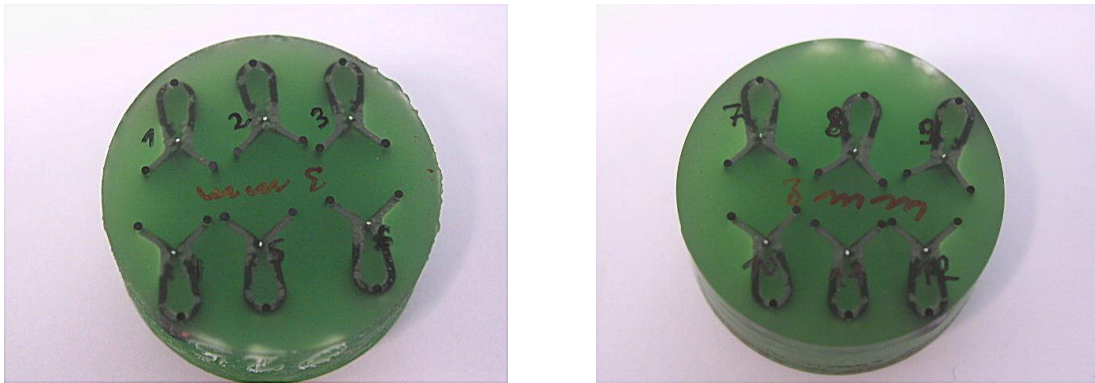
Aufgearbeitete Kunststoffscheiben.
